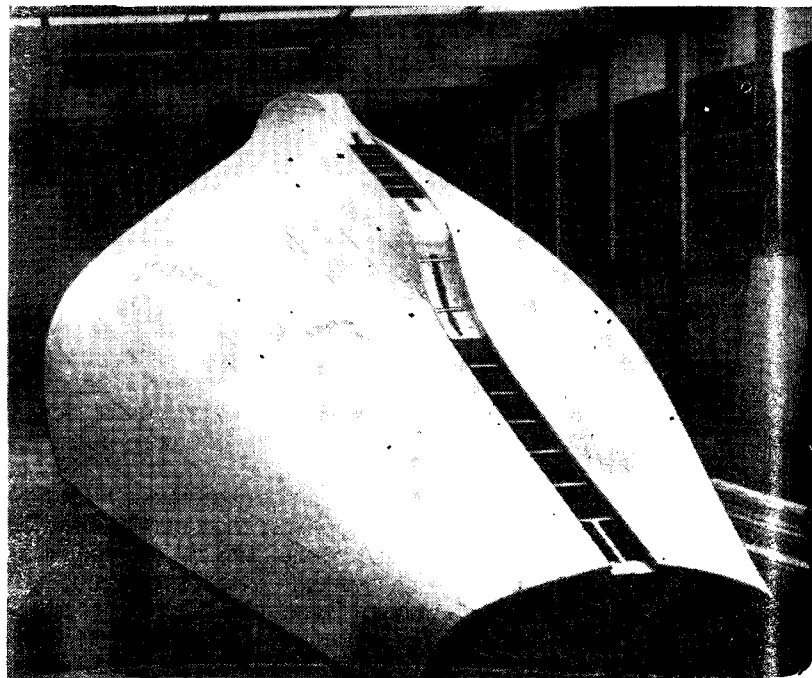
Болван — положительная форма, на которой строят клееные корпуса. Стоит примерно в два раза дороже, чем построенный по нему корпус.
